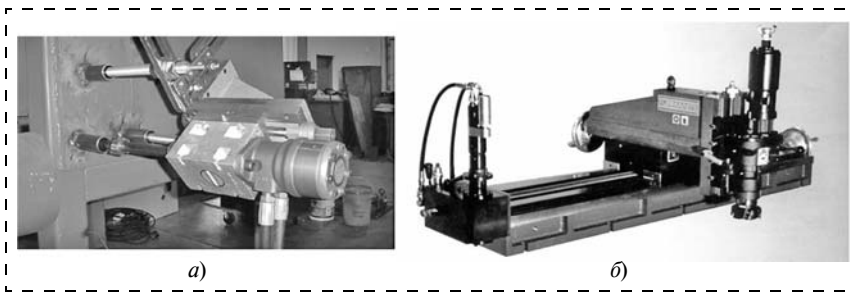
Портативное механообрабатывающее оборудование: а — сверлильный станок; б — фрезерный станок
